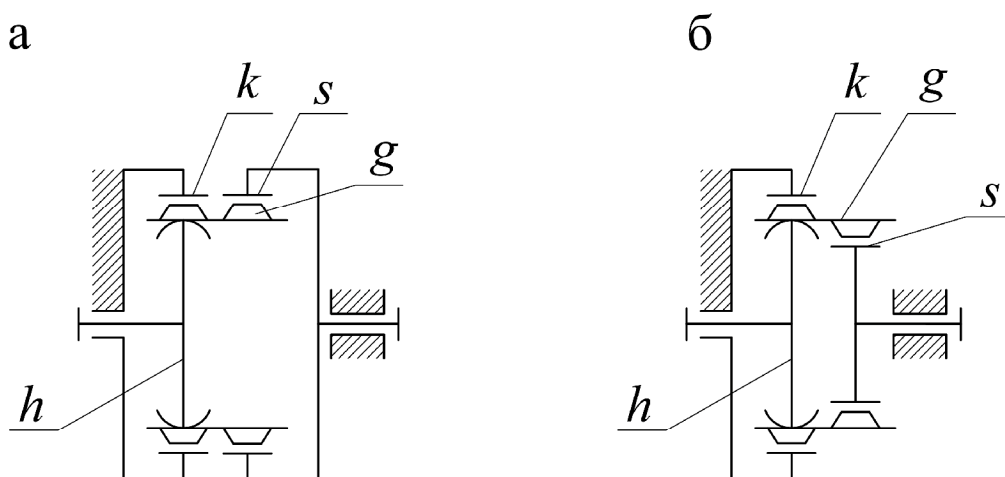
Кинематические схемы волновых передач с коротким гибким колесом; а – с жесткими колесами внутреннего зацепления, б – с жесткими колесами внутреннего и наружного зацепления;  $h$  – генератор;  $k, s$  – жесткие колеса;  $g$  – гибкое колесо
